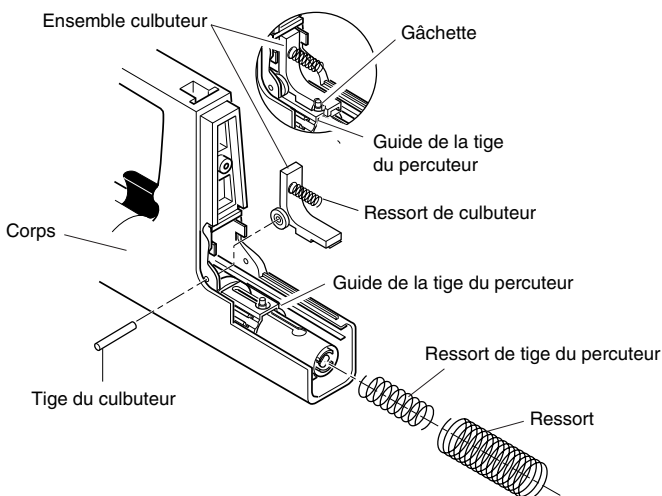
Remise en place du guide du percuteur, de l'ensemble percuteur, du ressort, de la tige de transfert et de la goupille-poussoir
